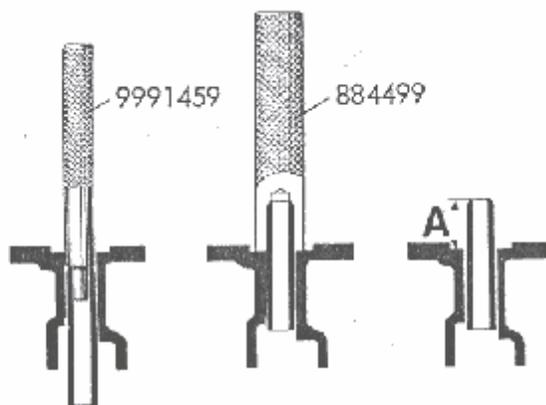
Werkzeug für Aus- und Einbau der Ventileführungen
